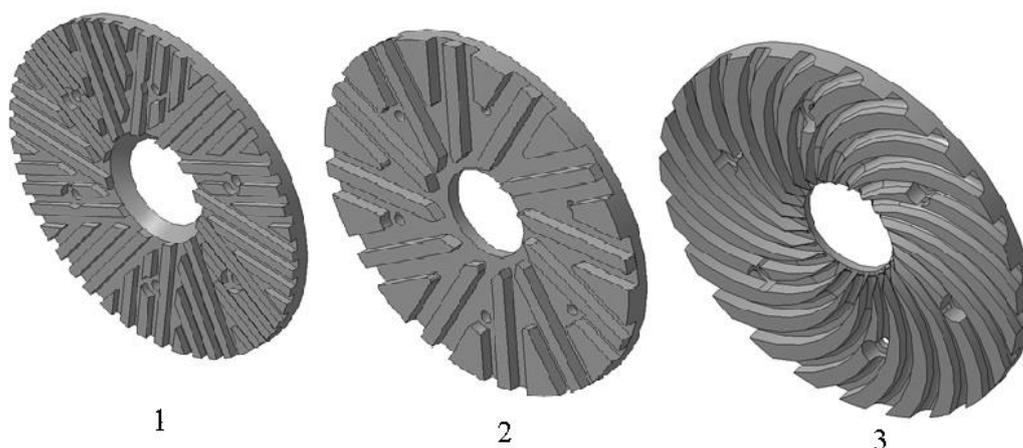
Конструкции размалывающих гарнитур: 1 – секторная с прямолинейной формой ножей и секундной режущей длиной 30990 м/с; 2 – прямолинейная с равномерным распределением ножей и секундной режущей длиной 22780 м/с; 3 – с эксцентрично окружными ножами (секундная режущая длина 33177 м/с)
